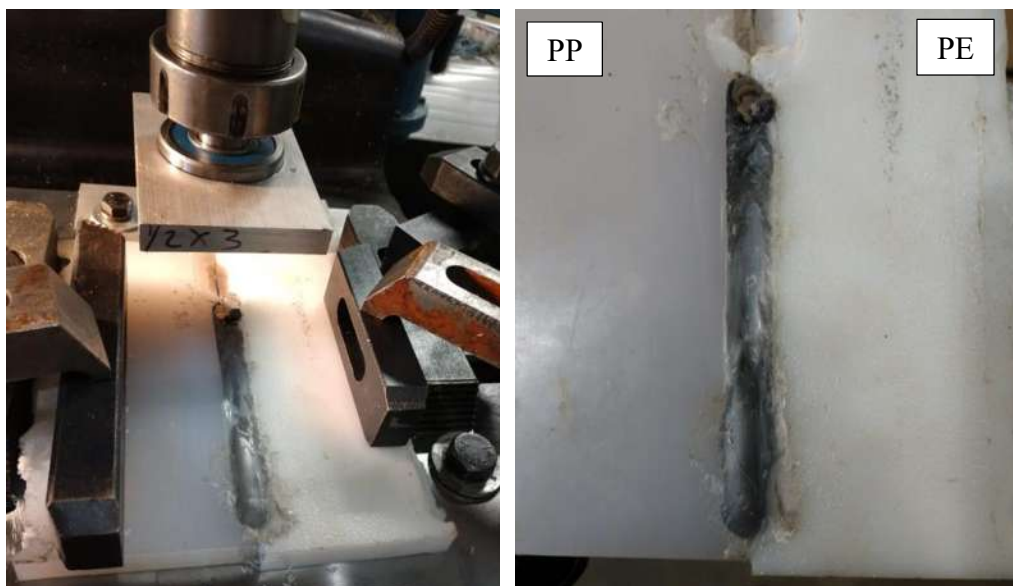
Hombro estacionario y cordón de soldadura PP – UHMWPE.
